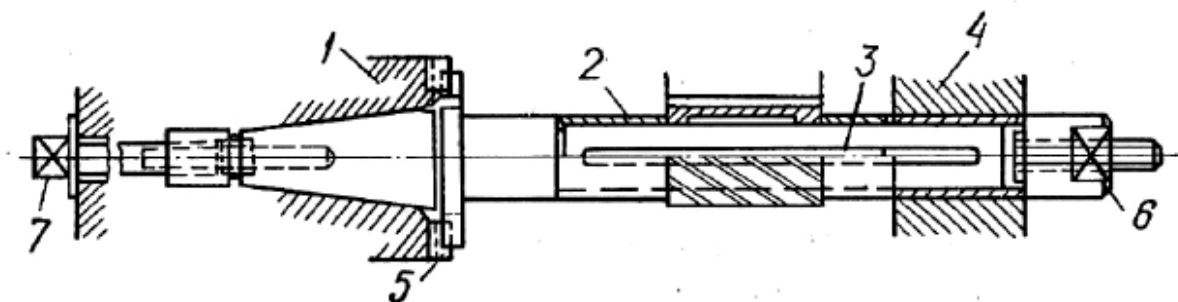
Закріплення фрези на центрових оправках: 1 – шпindel; 2 – установочні кільця; 3 – шпонка; 4 – підвіска; 5 – поводки; 6 – гайка; 7 - гвинт
